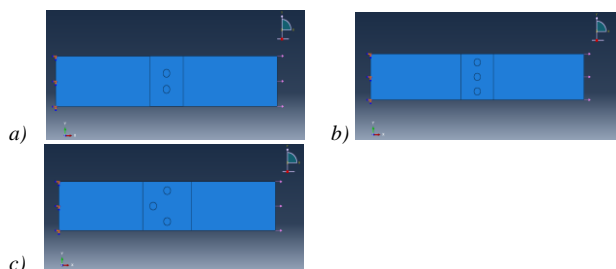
Assemblages des points soudés pour différentes positions : a) deux points de soudure ; b) trois points de soudure alignés ; c) trois points de soudure en triangle.
